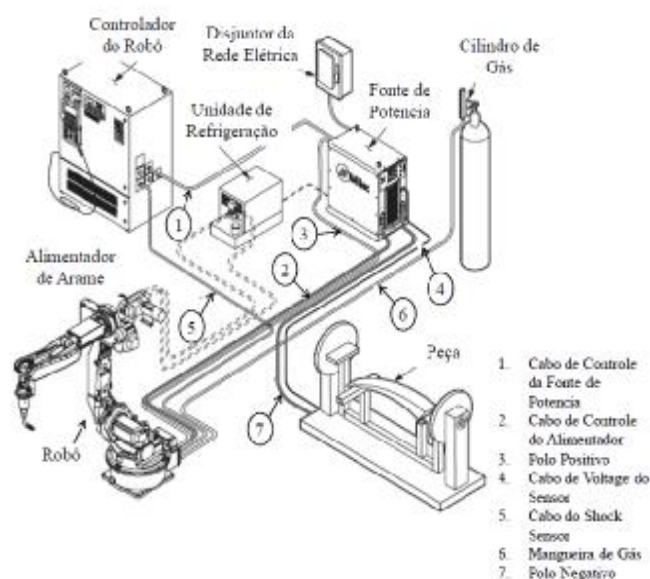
Representação esquemática de um sistema de soldagem robotizada.
